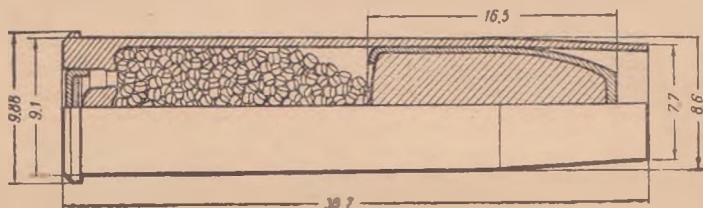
7,62-мм штатный револьверный патрон (размеры в мм)
